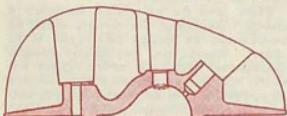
Конструкция цилиндра с вихревой камерой сгорания.
